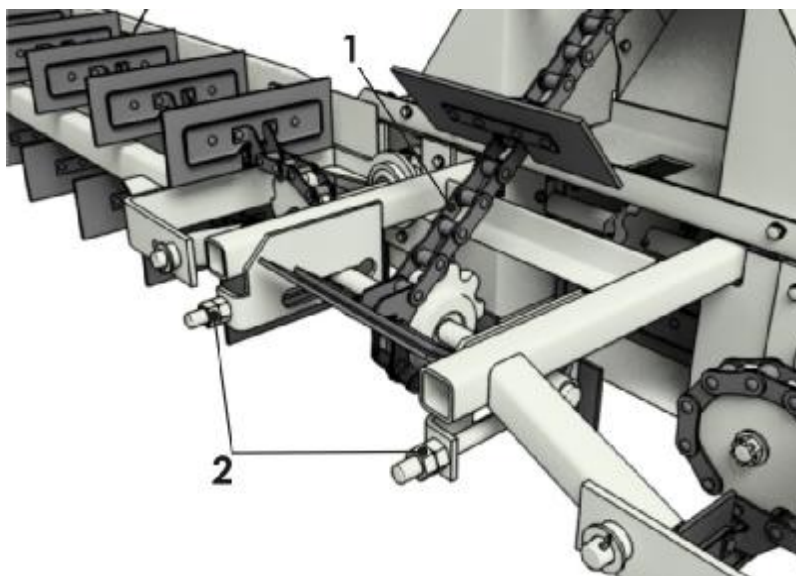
Регулировка натяжения скребковой цепи загрузочного транспортера
